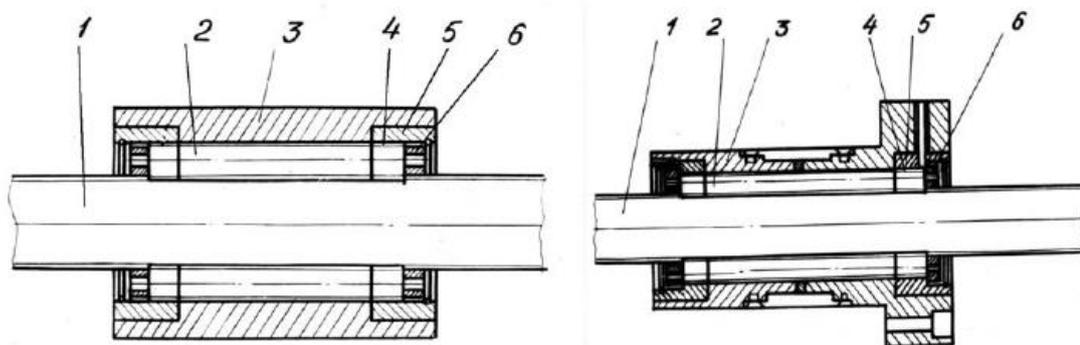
Передачи винт-гайка с короткими резьбовыми роликами:
